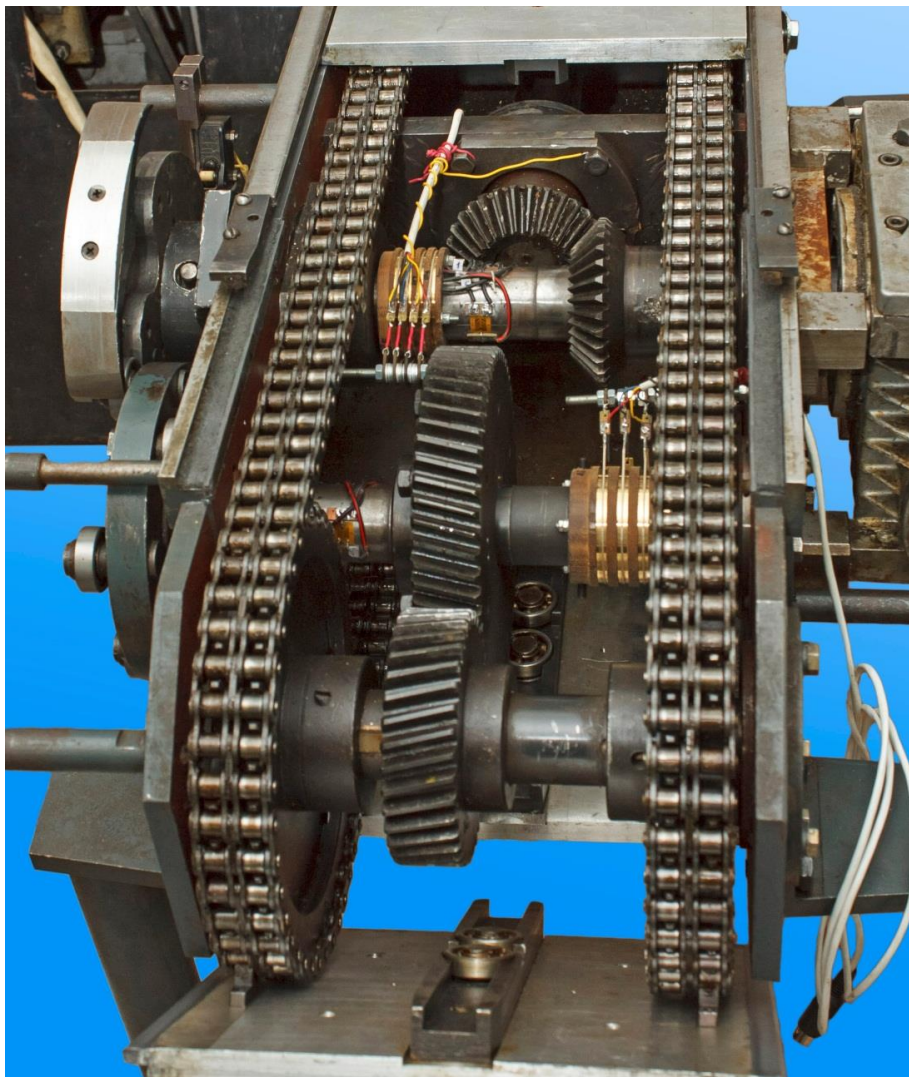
Кулачковий механізм привода транспортувального пристрою із змонтованими реєструвальними пристроями
